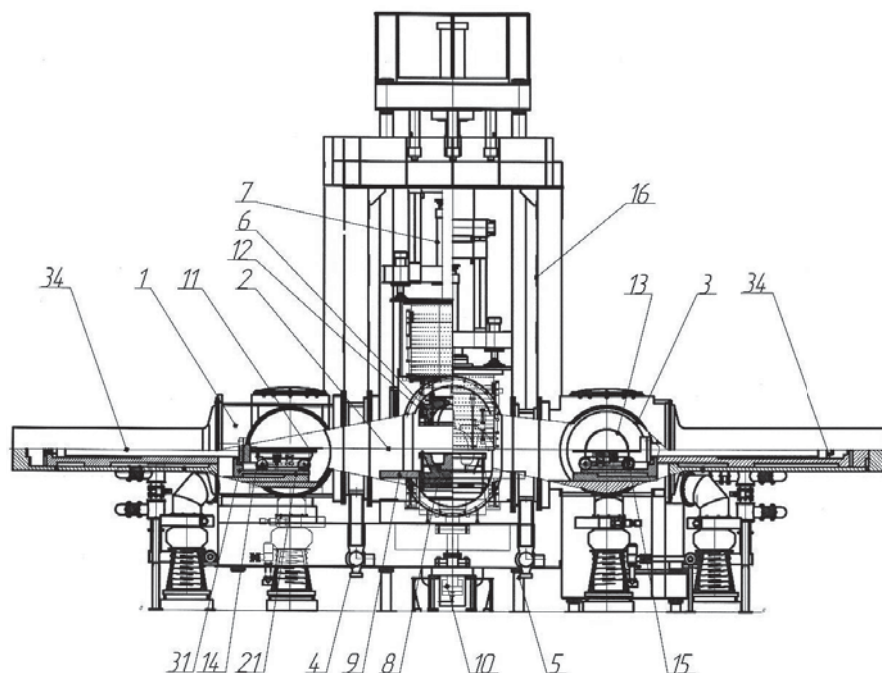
Схема вакуумной установки УСПД-1 для пневмоформовки полусфер шаробаллонов
